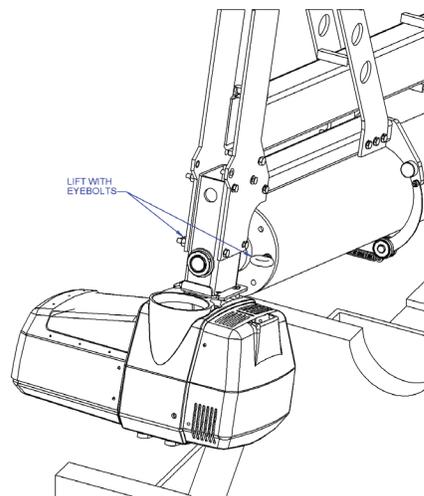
E. Rimozione del dispositivo Easy Arm® dall'imballaggio.
